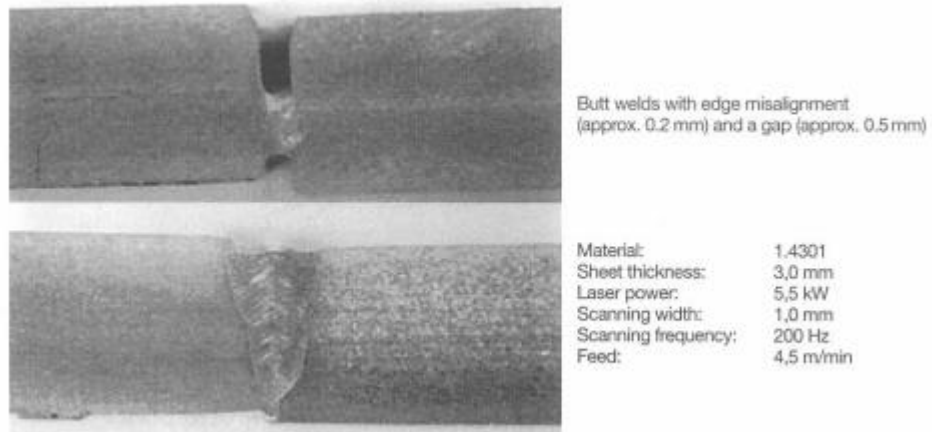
Processo de soldadura laser com e sem a deflexão do feixe, [2].
